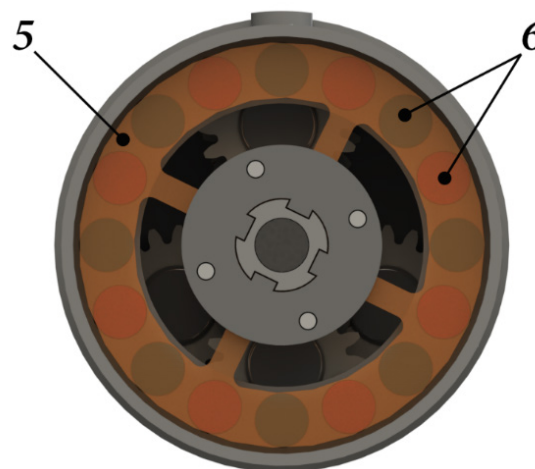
Магнитный (вихретоковый) тормоз:
